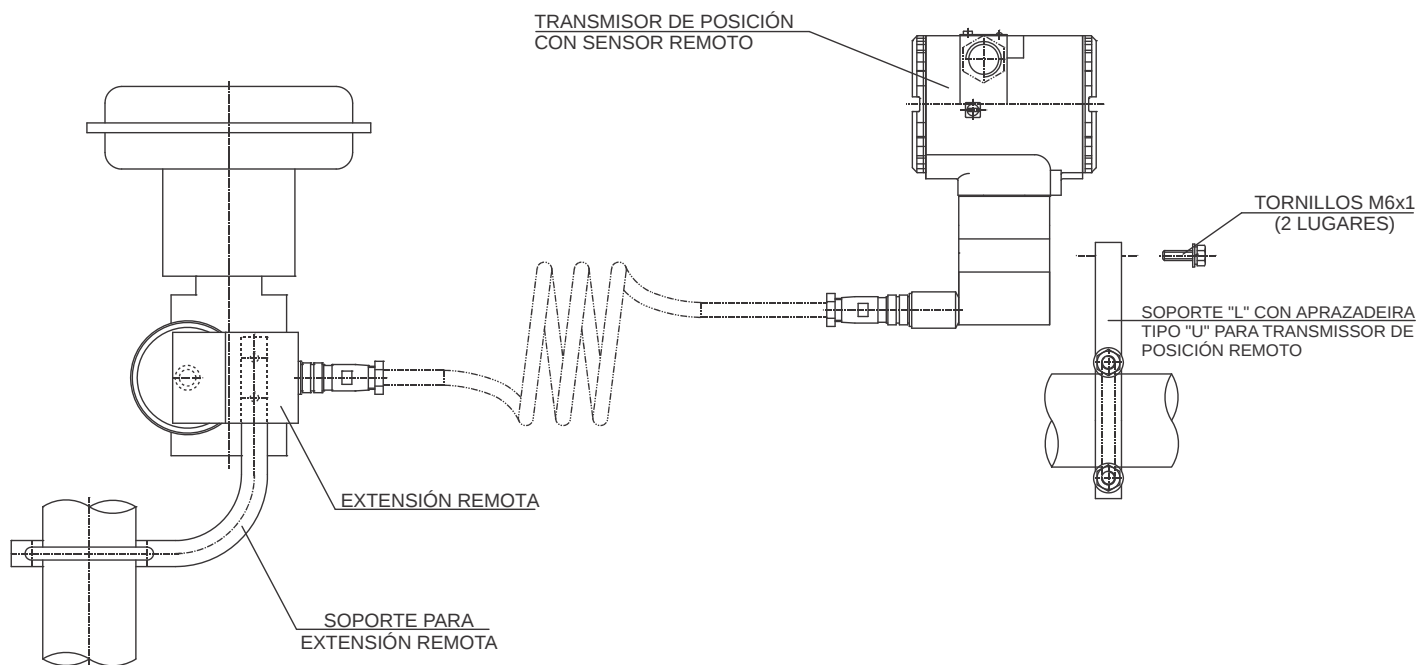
Transmisor de Posición en Actuador Rotativo con Sensor de Posición Remoto
